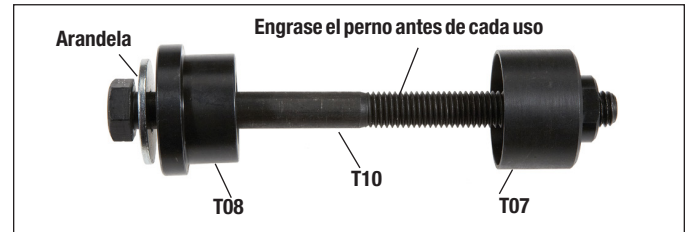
Herramienta de instalación de tubo de guía de pasador guía corto
